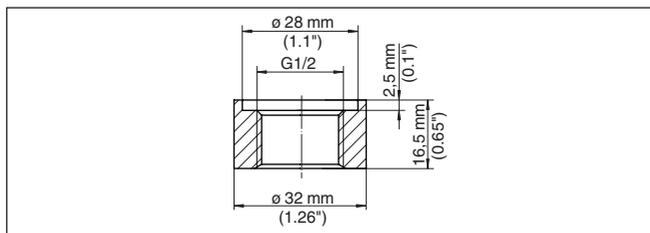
Dimensiones racor para soldar rosca G $\frac{1}{2}$ (DIN 3852-X)
